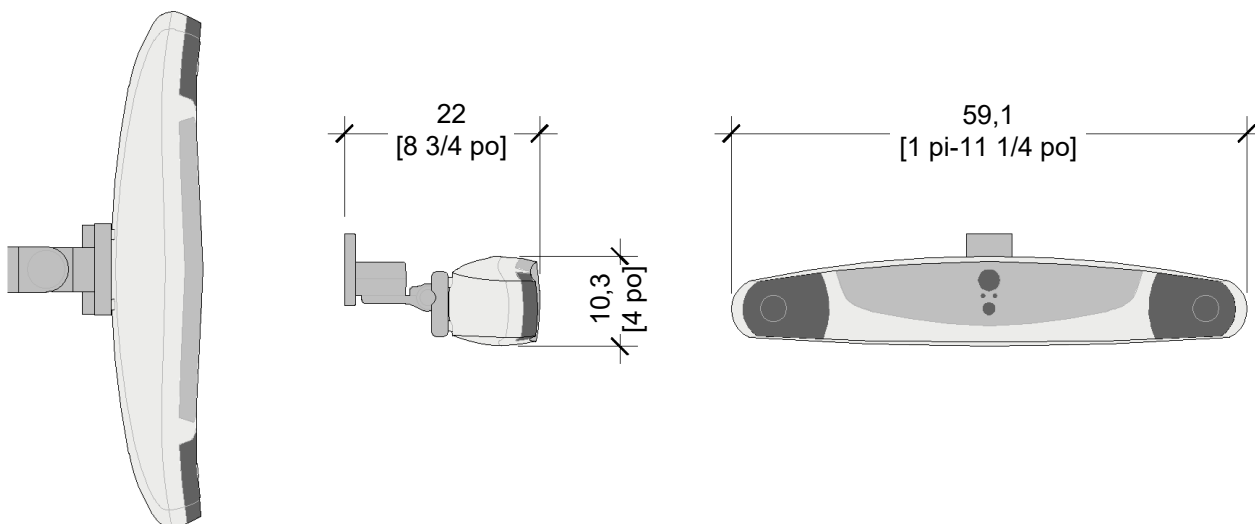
Imageur optique SGC (vue de dessus, vue latérale et vue de face)
